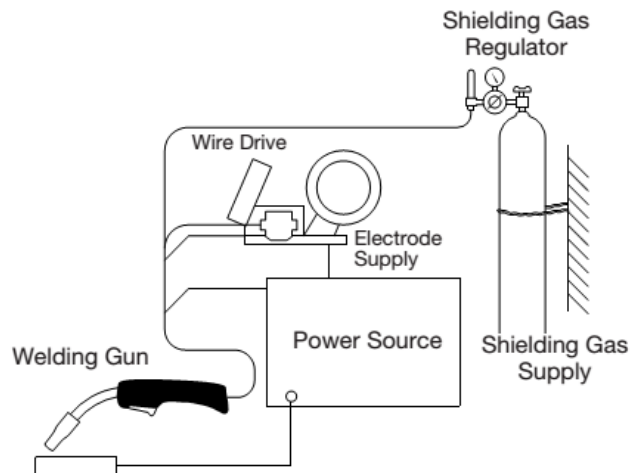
Esquema de uma máquina de soldadura MIG/MAG [9]
